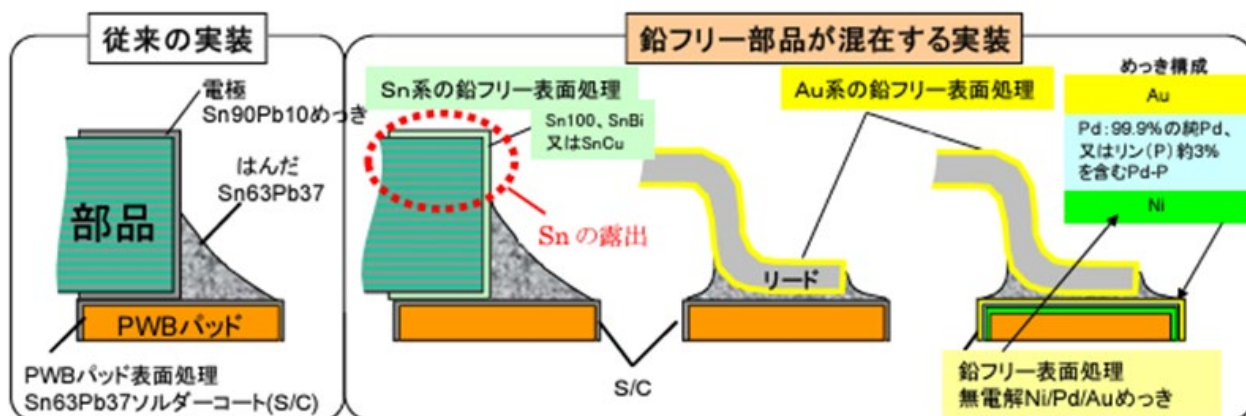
Mixed Assembly (鉛フリー部品が混在する実装)のモデル
